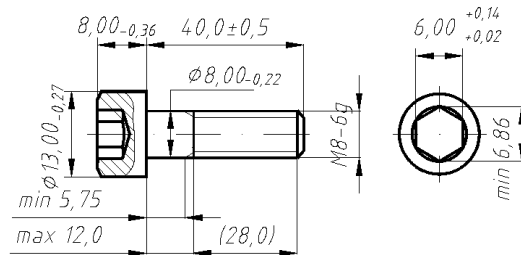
Винт с цилиндрической головкой и шестигранным углублением под ключ
